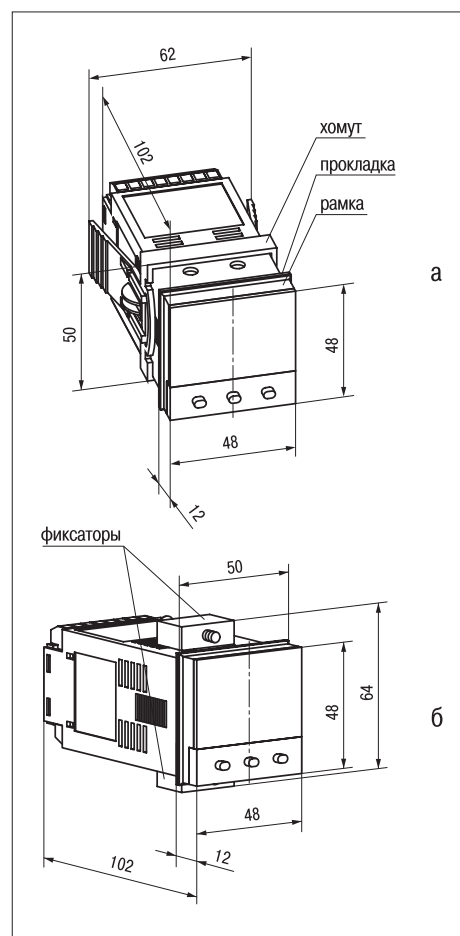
Корпус ТРМ101: а — крепление хомутом; б — крепление фиксаторами
